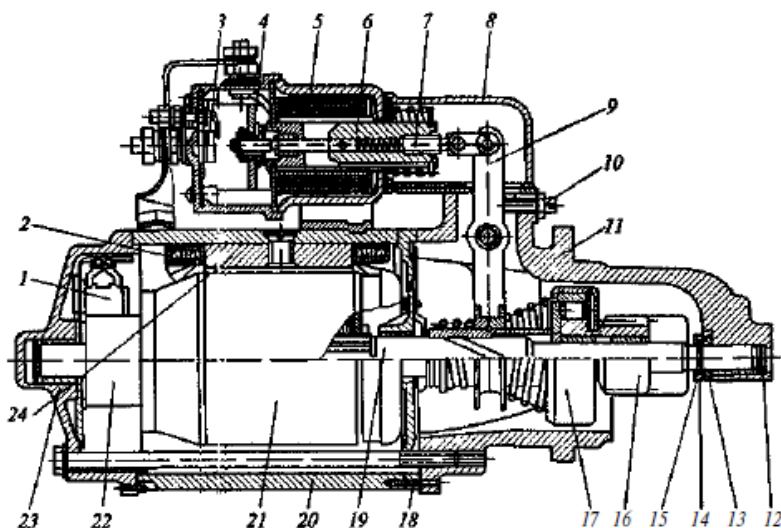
Электростартер с радиально расположенными щетками: 1 – щетки; 2 – обмотка статора; 3 – контакты тягового реле; 4 – подвижный контакт; 5 – обмотки тягового электромагнита; 6 – якорь; 7 – тяга; 8 – кожух; 9 – рычаг; 10 – винт регулировки хода шестерни; 11 – крышка со стороны привода; 12 – фальц с заглушкой; 13 – втулка; 14 – замковая шайба; 15 – антифрикционная шайба; 16 – шестерня привода; 17 – муфта свободного хода; 18 – промежуточная опора; 19 – вал якоря; 20 – корпус стартера; 21 – сердечник якоря; 22 – коллектор; 23 – крышка; 24 – сердечник обмотки возбуждения
